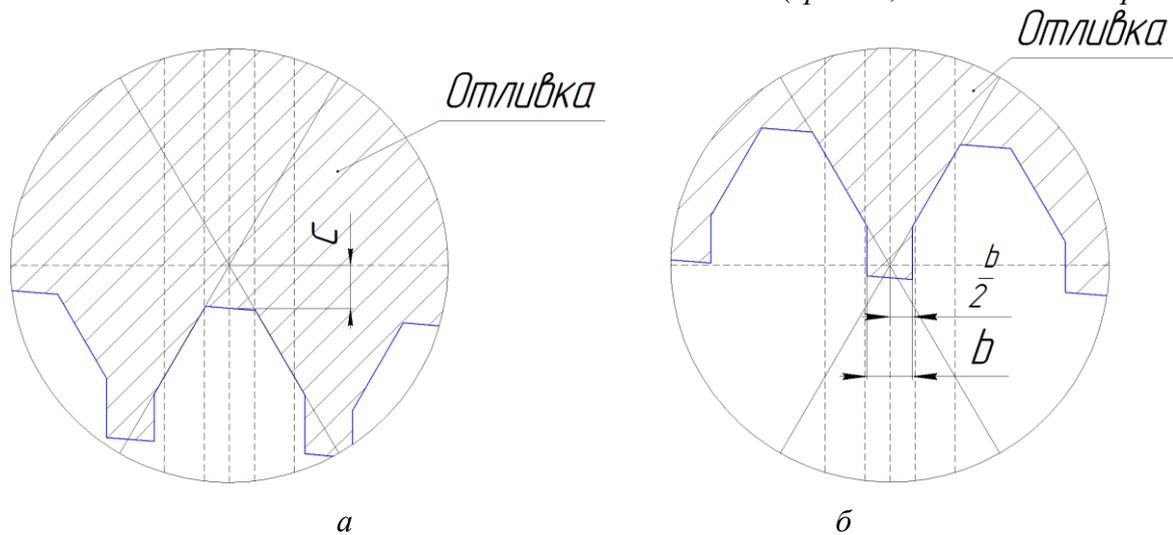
Схема измерения величины среза вершины треугольного профиля резьбы
